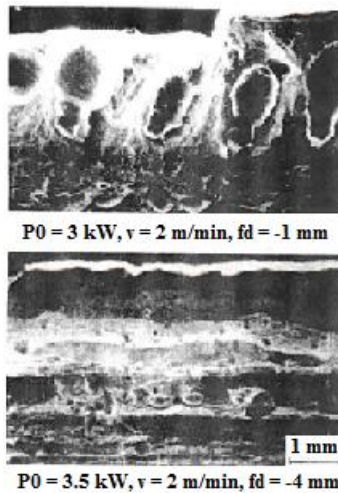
Microfotografías electrónicas de barrido de dos cordones fracturados en la zona de fusión de soldadura láser de la aleación AA2090 se muestra la formación de porosidad en función de las condiciones de la soldadura. Por Katayana (1989).
